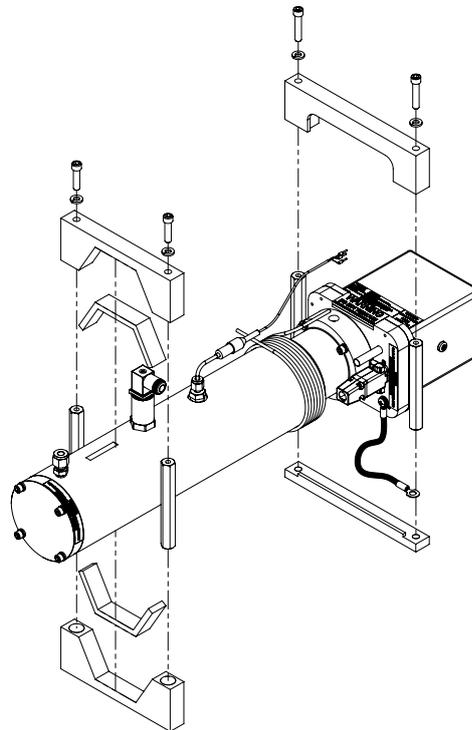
Zeichnung der Montagehalterung für die 28m- oder 8m-Messzelle
